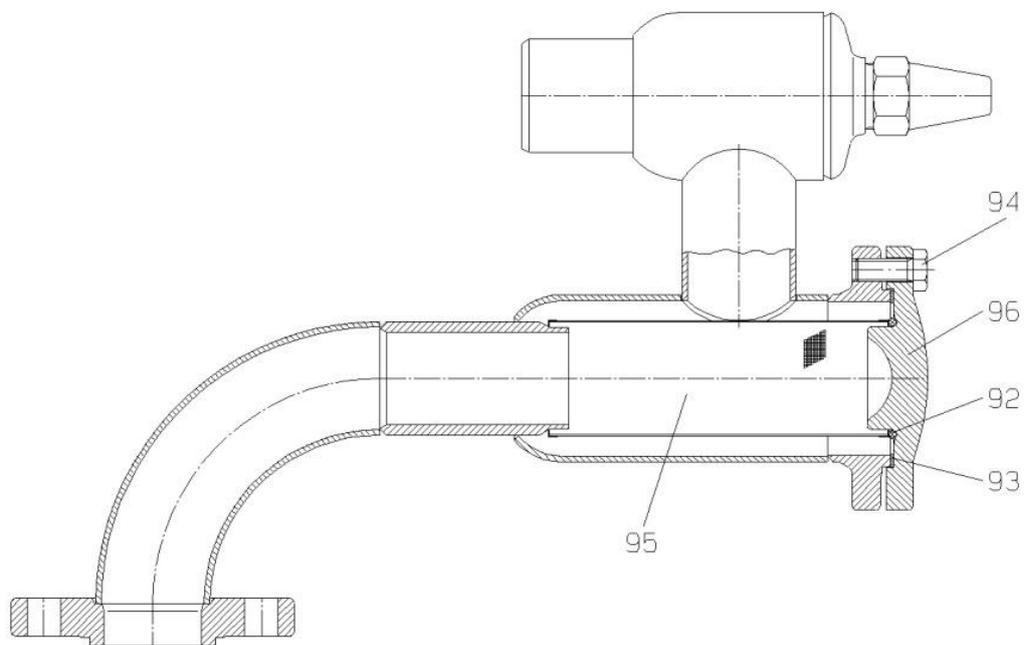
Детальный чертеж входного фильтра KS 40-P/KS 50-P
